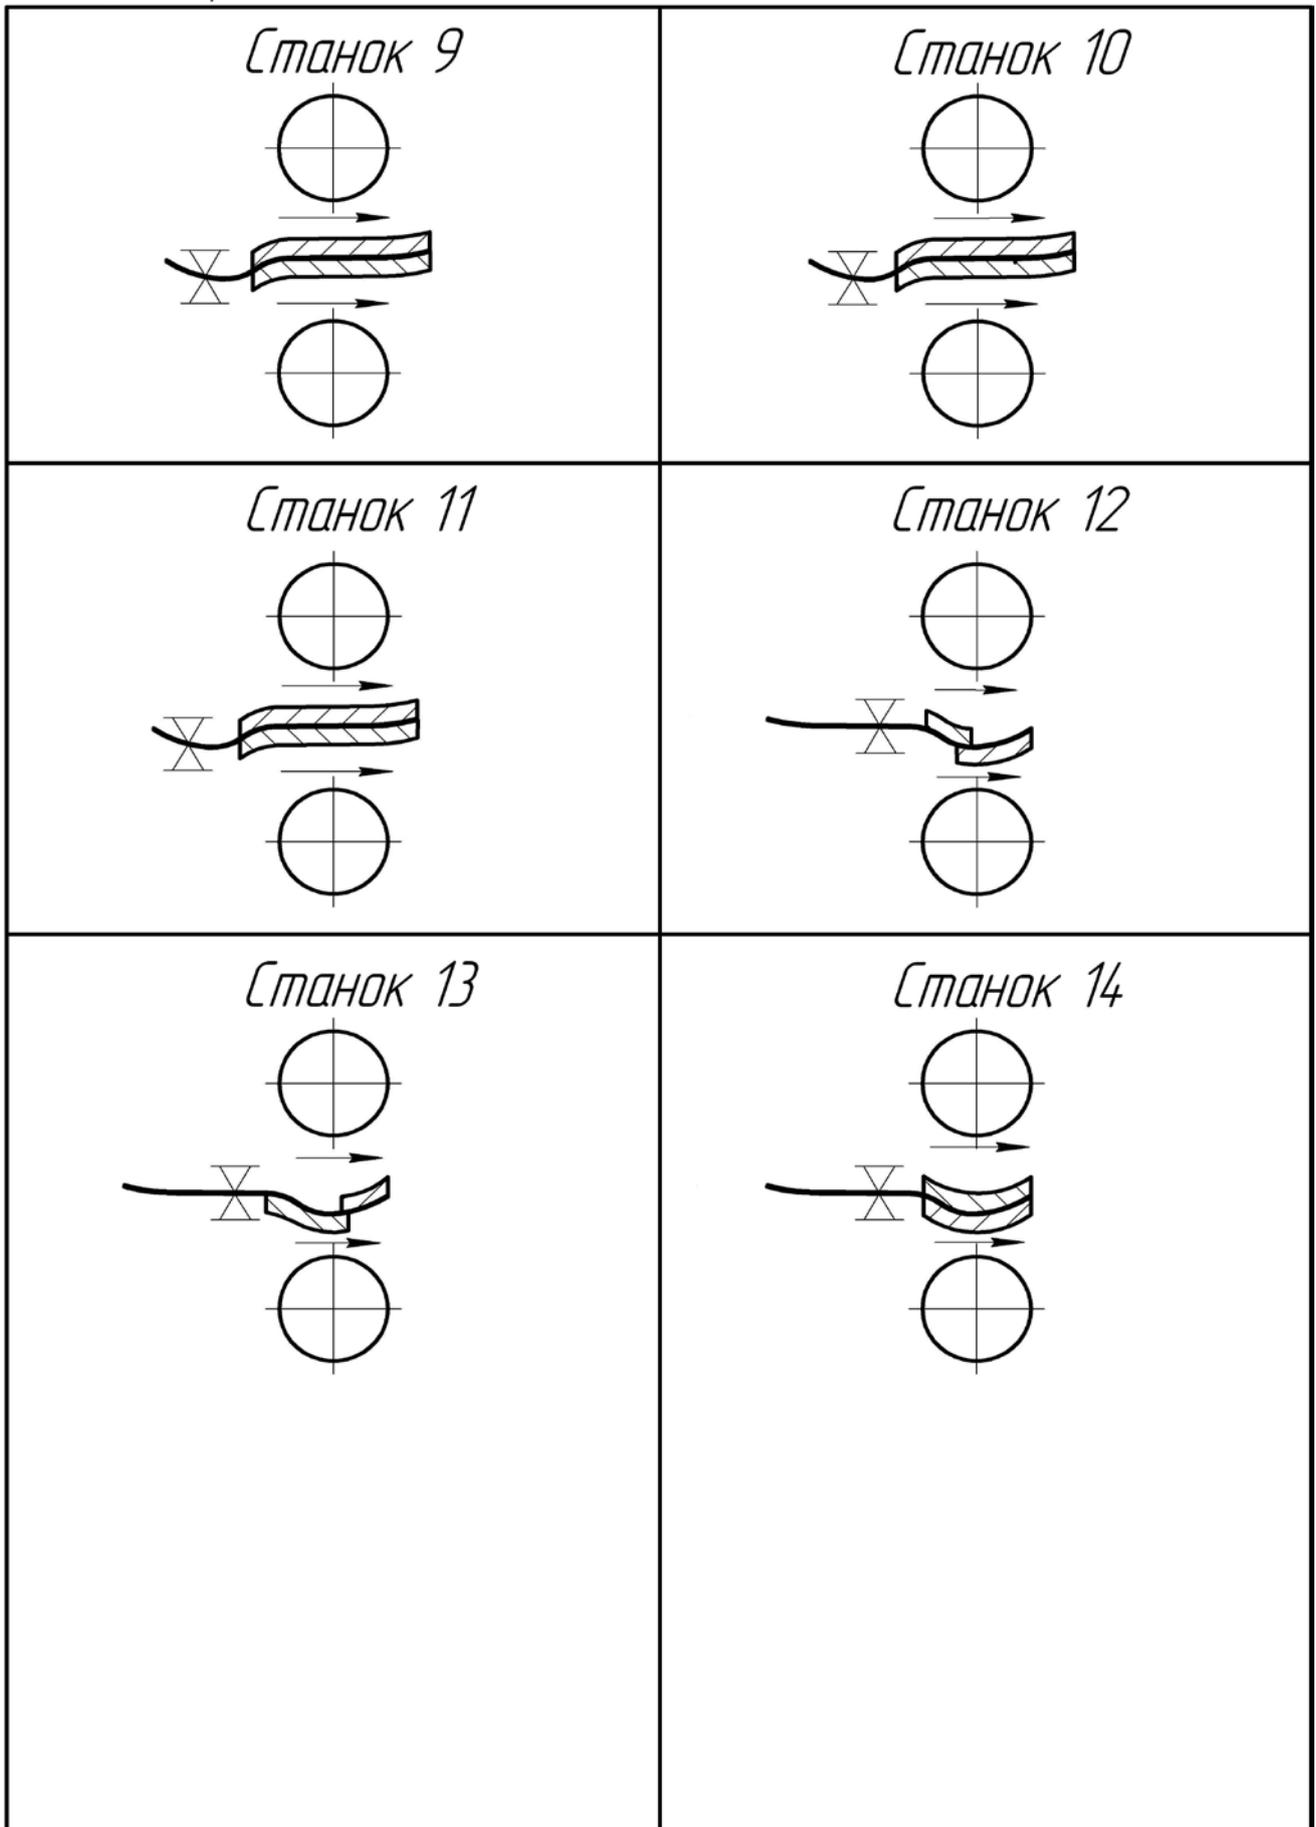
Области обрабатываемой поверхности изделия
